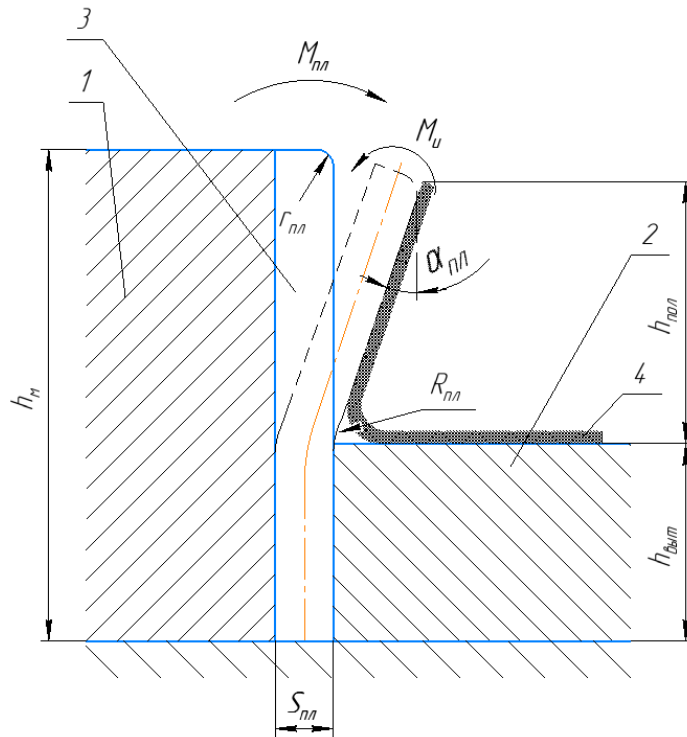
Схема к расчету упругой билинейной планки:
